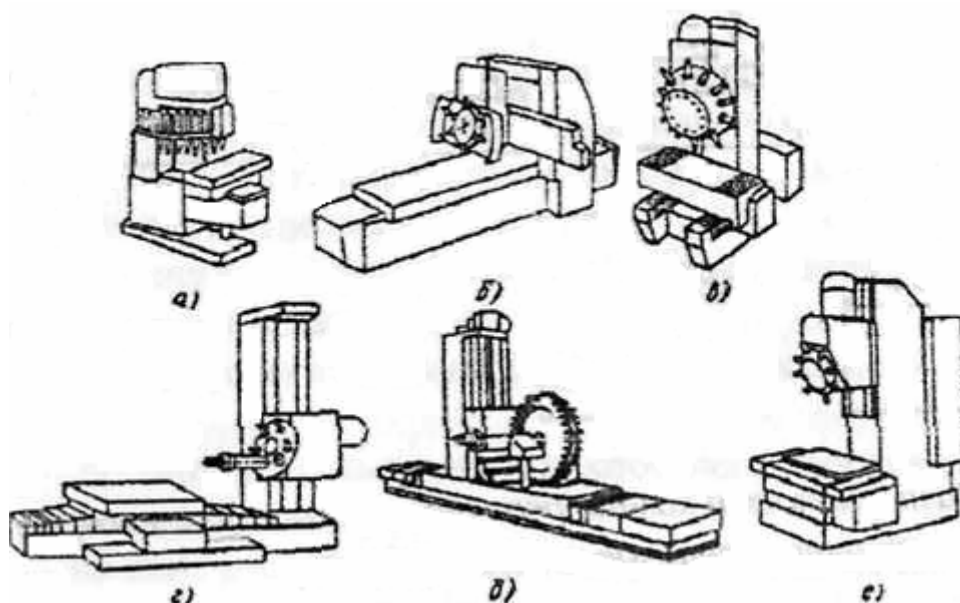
Многооперационные станки по типу традиционных компоновок станков: а, б – фрезерных; в – вертикально-фрезерных или координатно-расточных; г, д – горизонтально-расточных; е – агрегатных сверлильно-расточных
